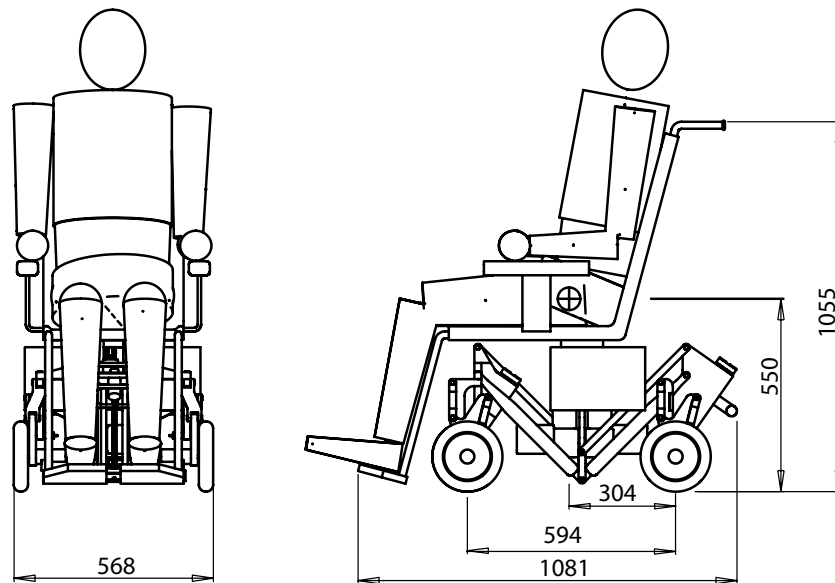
Dimensiones del conjunto y posición del centro de gravedad.
